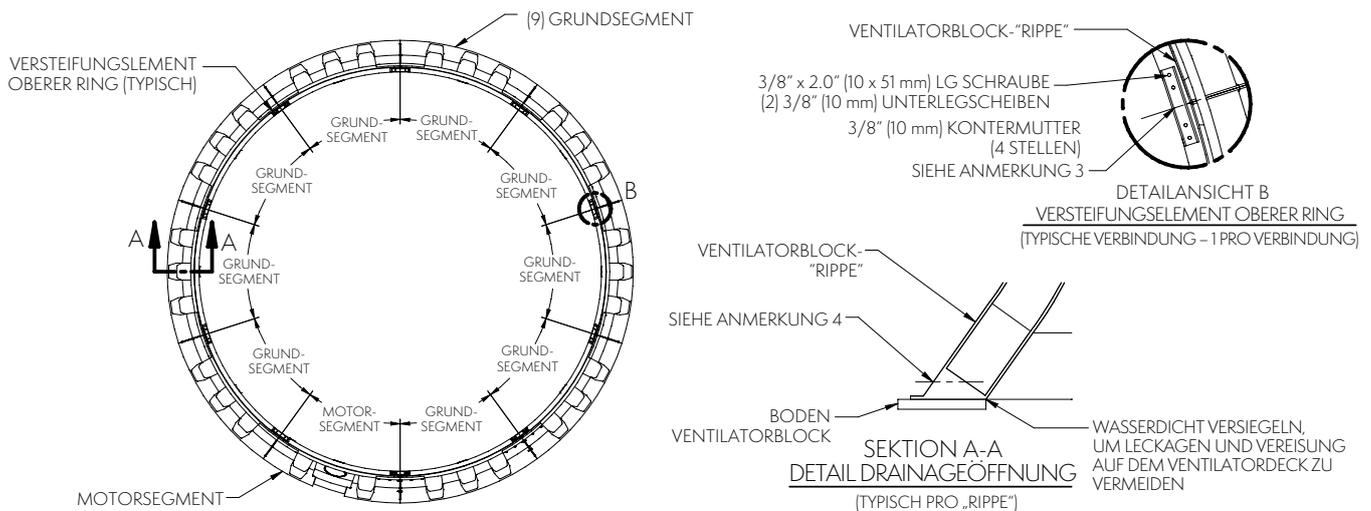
Typische Grundrissansicht eines Ventilatorblock
